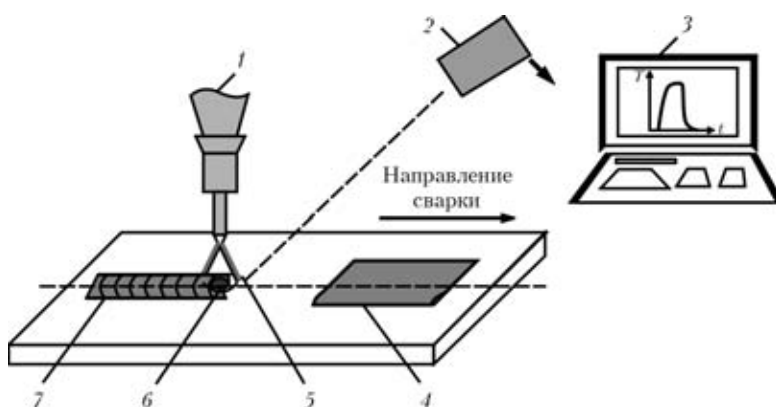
Схема проведения эксперимента: 1 — горелка; 2 — пирометр; 3 — компьютерная система с программным обеспечением; 4 — активатор; 5 — дуга; 6 — сварочная ванна; 7 — шов
